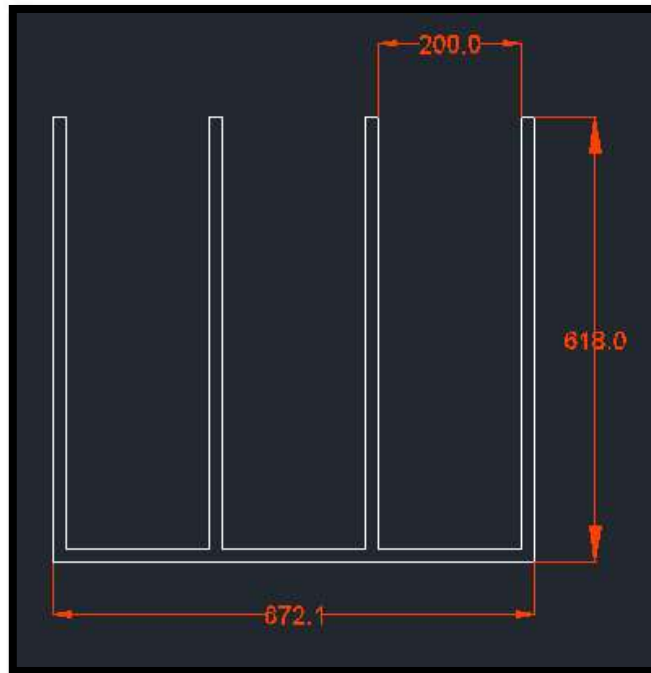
Diagrama estructura metálica – Vista frontal.
